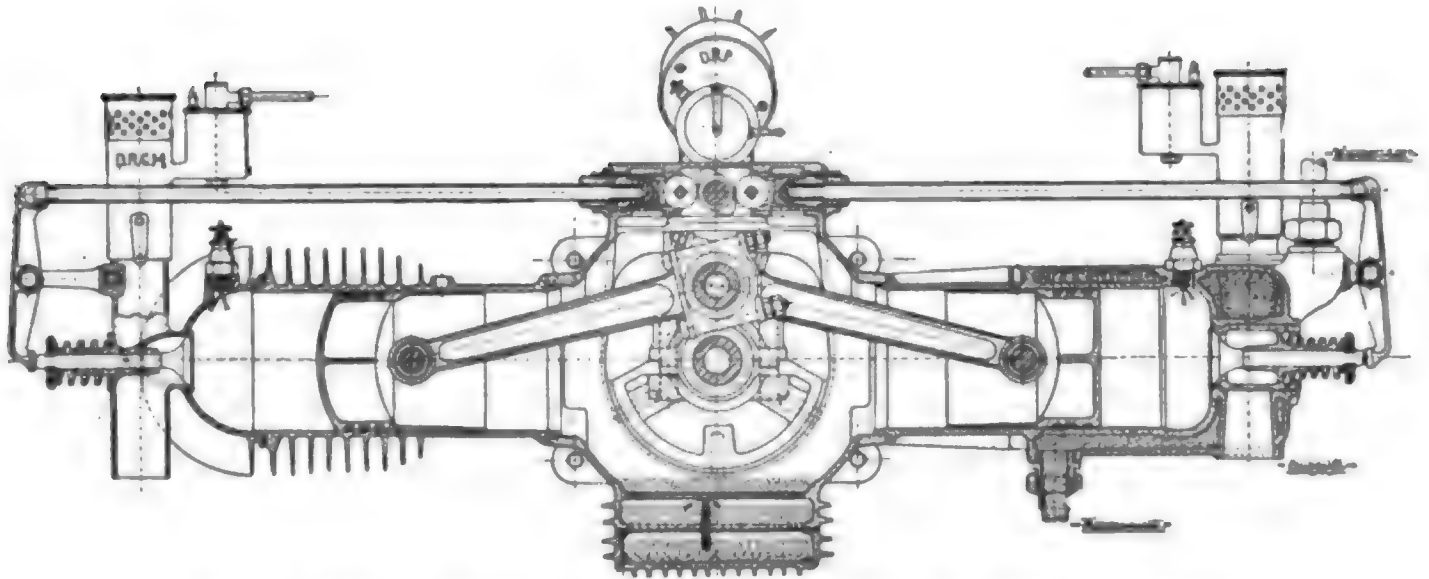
Zeichnung des Flugmotors von Escher & Co., mit liegenden Zylindern. Querschnitt.
